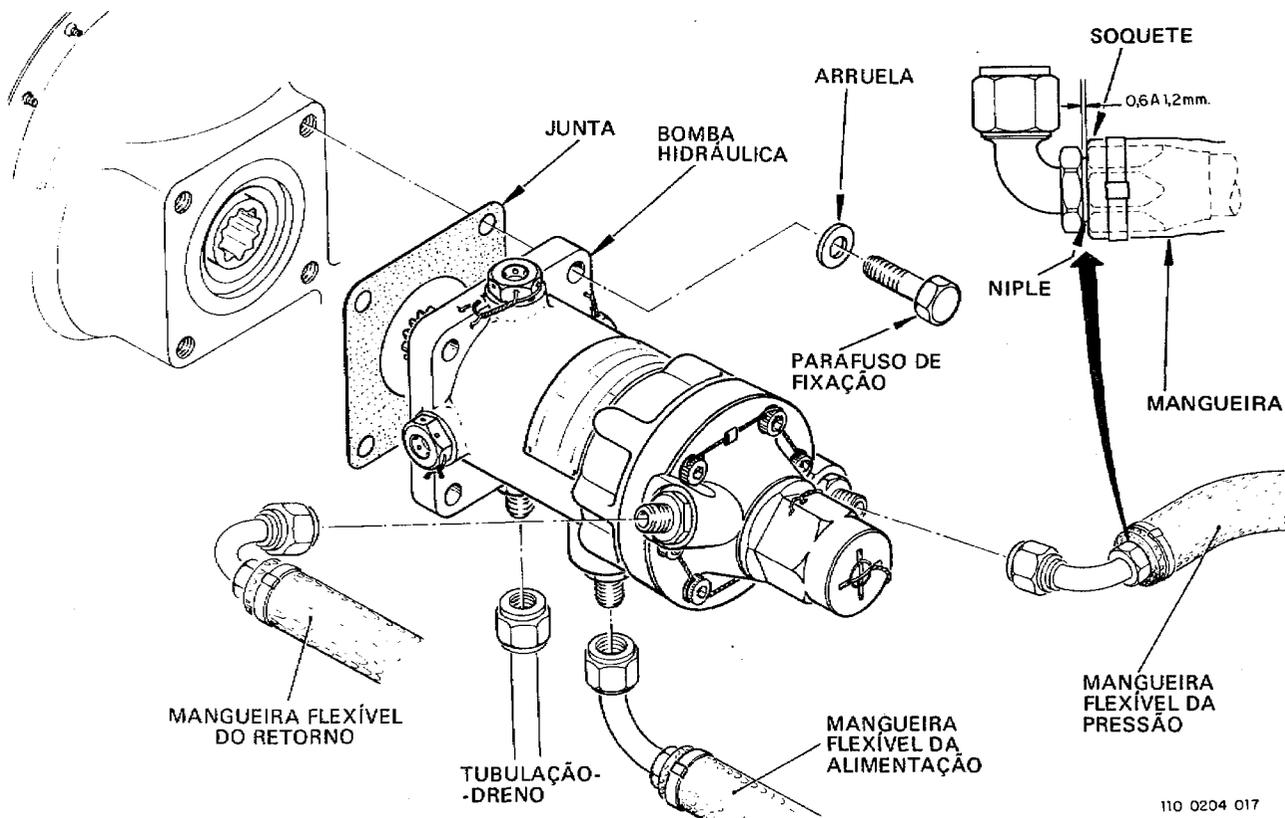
Instalação da Bomba Hidráulica (NEW York Air Brakes)
